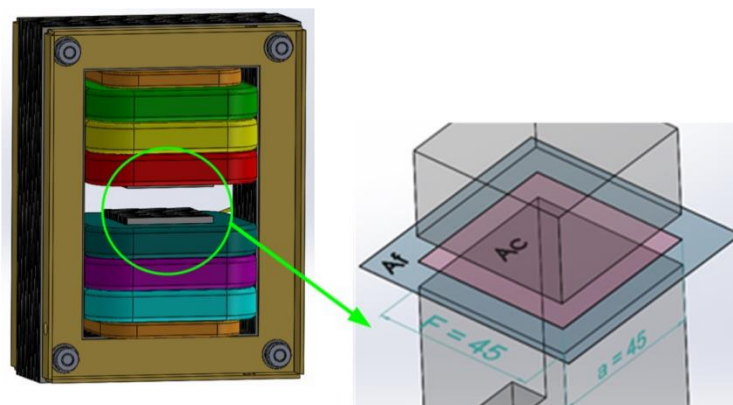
Plano central do entreferro (núcleo em corte).
